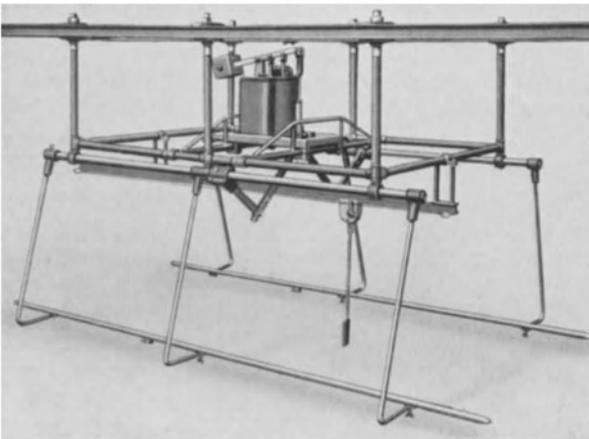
Selbsttätige Furnierablegervorrichtung (Maschinenfabrik C. Müller, Forst über Holzminden).
